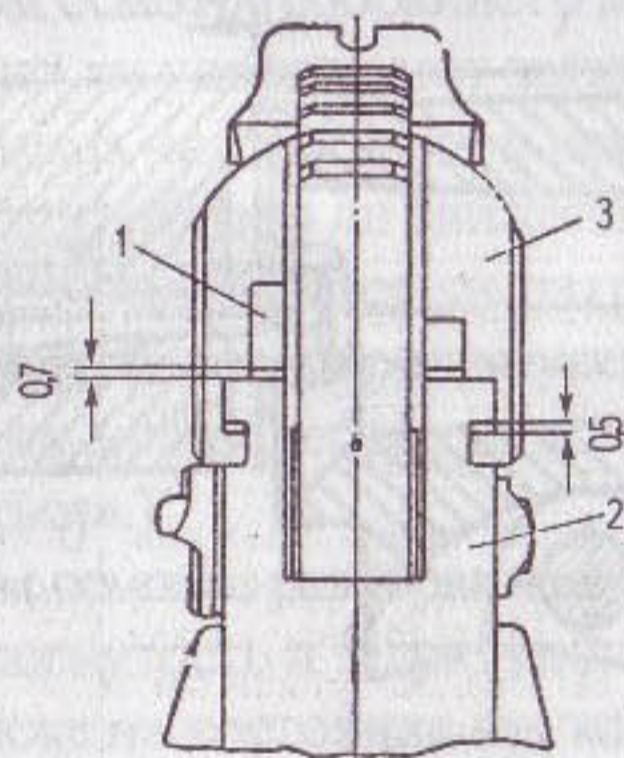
Допускаемые зазоры (в мм) между выступами рамки и пазами затвора: 1 — колодка ударно-спускового магазина; 2 — рамка; 3 — затвор
